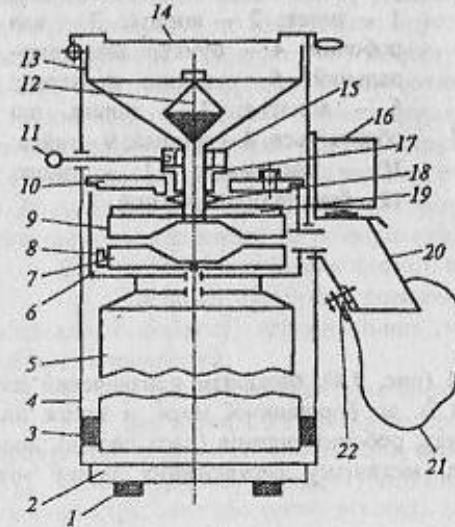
Дискова машина для розмельювання кави МИК-60: 1 – опора гумова; 2 – основа; 3 – амортизатор гумовий; 4 – корпус; 5 – електродвигун; 6 – камера робоча; 7 – жорно, що обертається; 8 – лопатка; 9 – жорно нерухоме; 10 – кришка знімна; 11 – рукоятка; 12 – пастка магнітна; 13 – бункер завантажувальний; 14 – кришка відкидна; 15 – кільце; 16 – електровібратор; 17 – втулка різьбова; 18 – пружина демпферна; 19 – фланець; 20 – труба; 21 – пакет; 22 – планка
